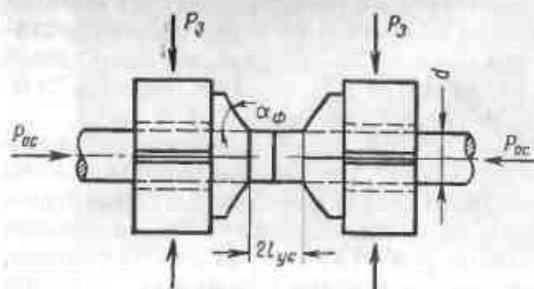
Схема прессовой сварки с принудительным формированием стыка [127]
